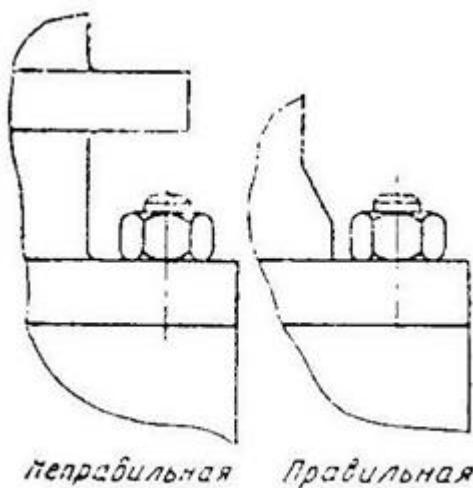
Примеры соединений, не пригодных для автоматической сборки
